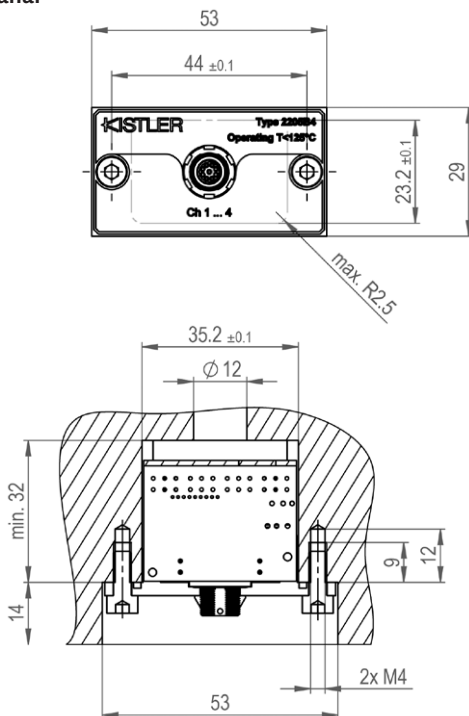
Abmessungen und Einbaumasse – 4-Kanal
